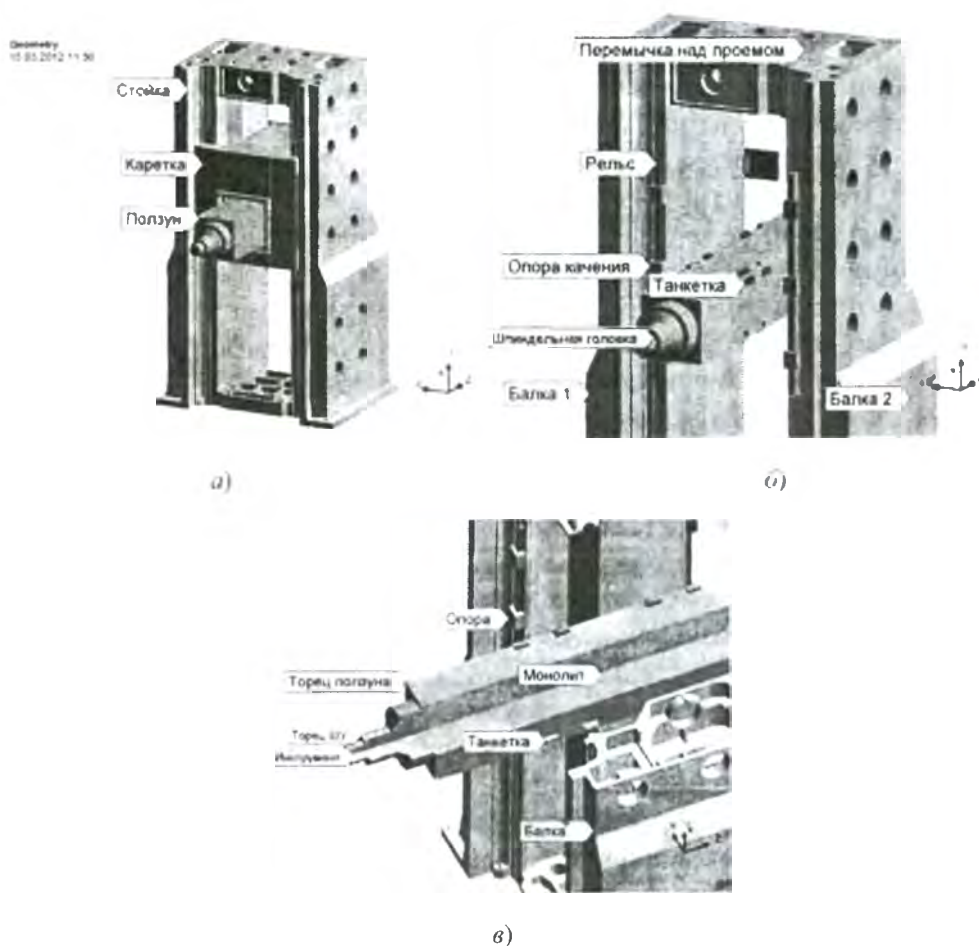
Стойка фрезерно-сверлильно-расточного станка (а); геометрическая модель сопряженных деталей стойки (каретка не показана) (б); геометрия оребрения балки (в)
